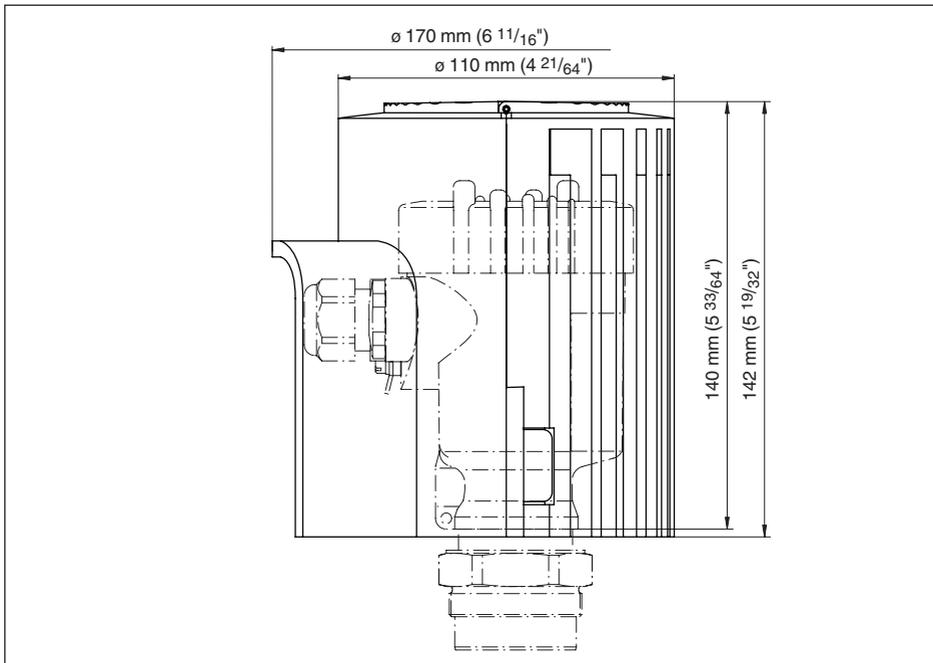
Ausführung für Gehäuse mit zentrischem Kabelanschluss
